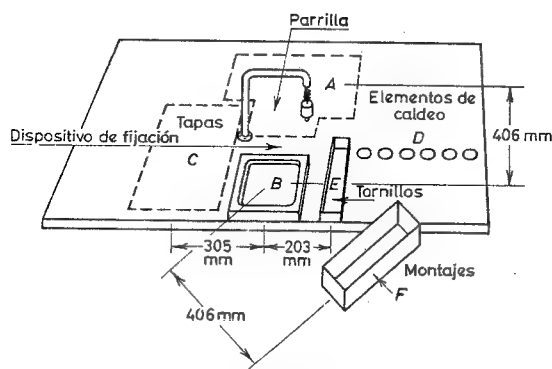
Disposición del lugar de trabajo para el montaje de elementos de caldeo.
